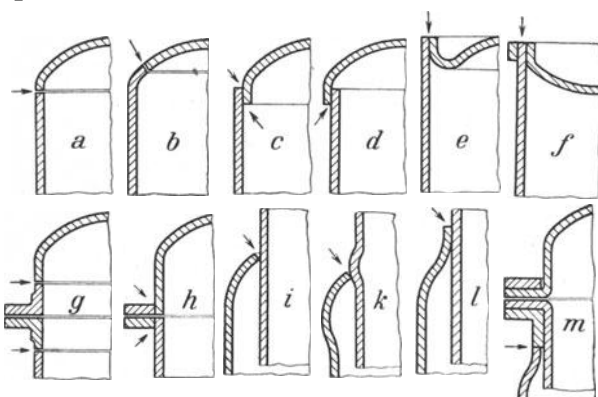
Anordnung der Schweißnähte an geschlossenen Behältern.
